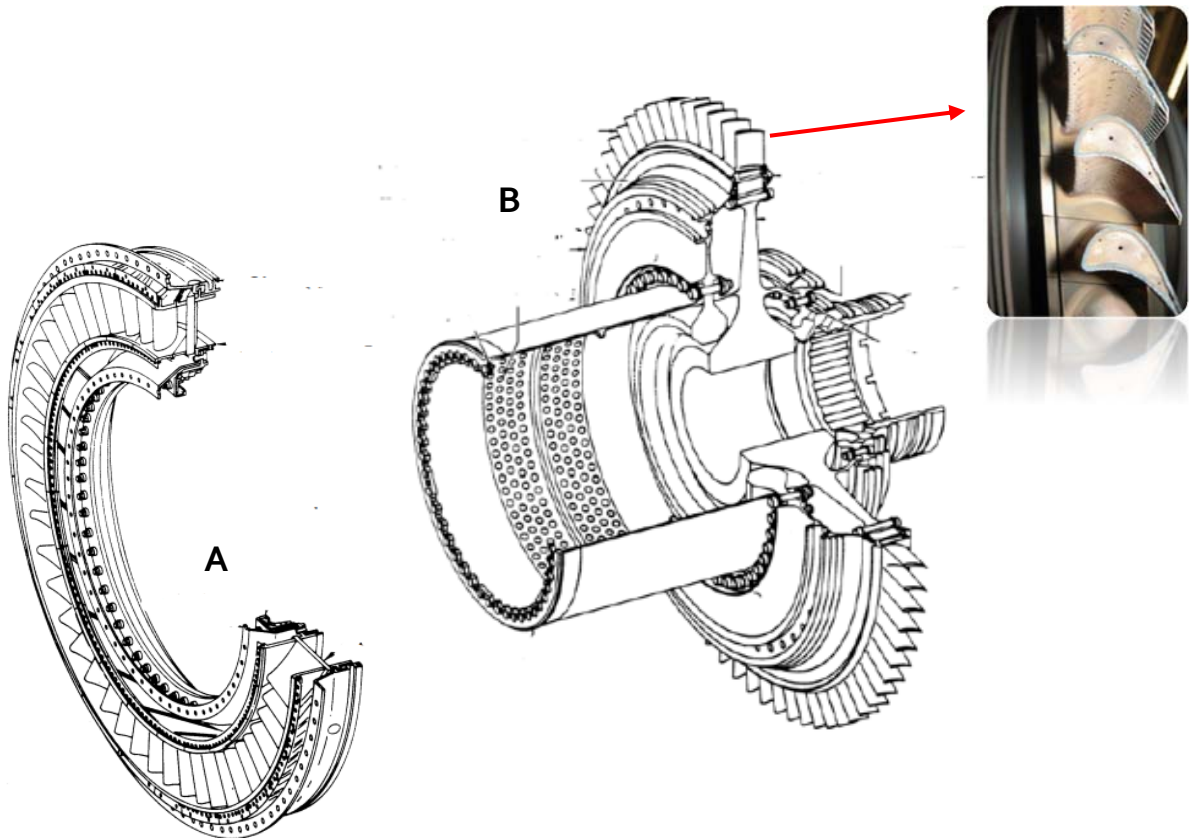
Etapa de turbina alta presión del CFM56 [26]
